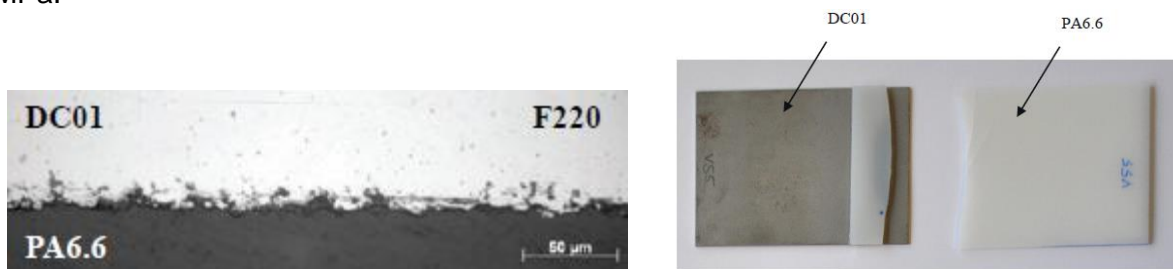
Vue en coupe à l'interface d'un joint soudé acier DC01 / PA6.6 et profil de rupture [62]
